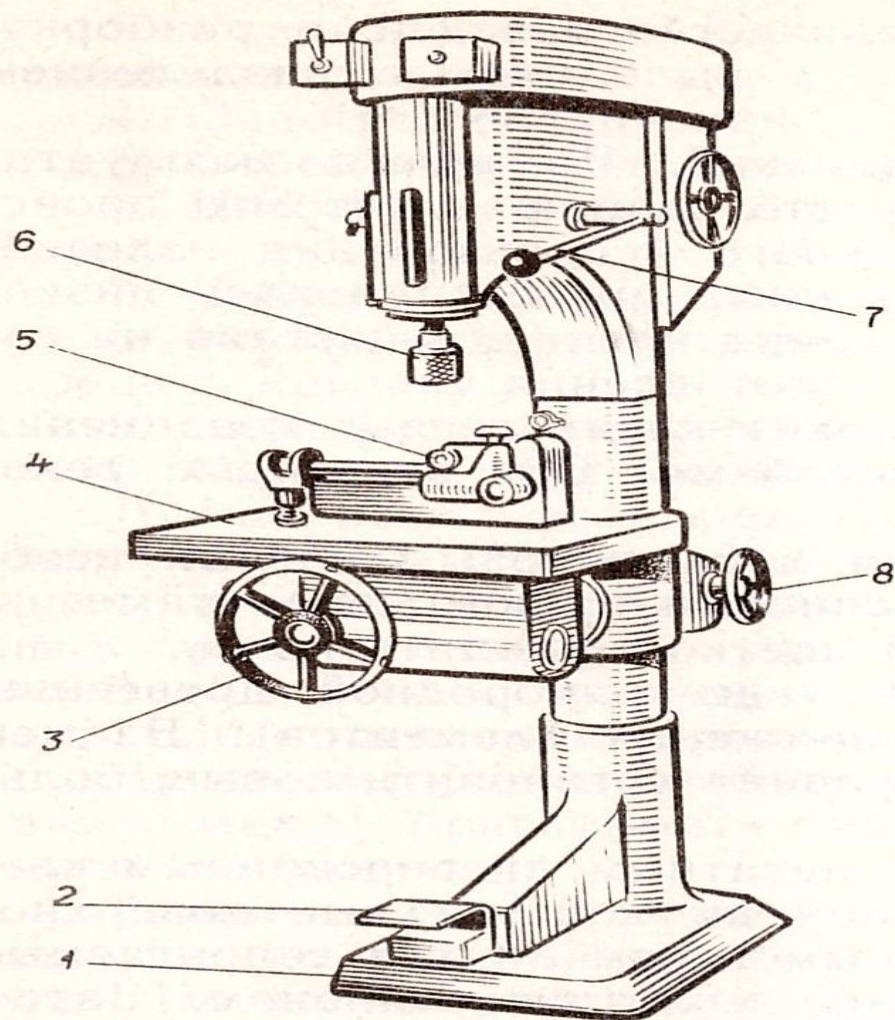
Вертикальный сверлильно-пазовальный станок:
